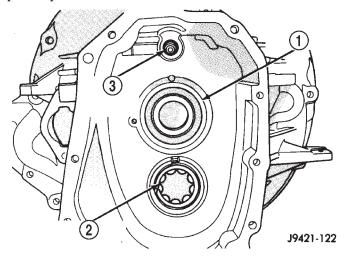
COJINETE DELANTERO DEL EJE IMPULSOR Y ARBOL INTERMEDIARIO
